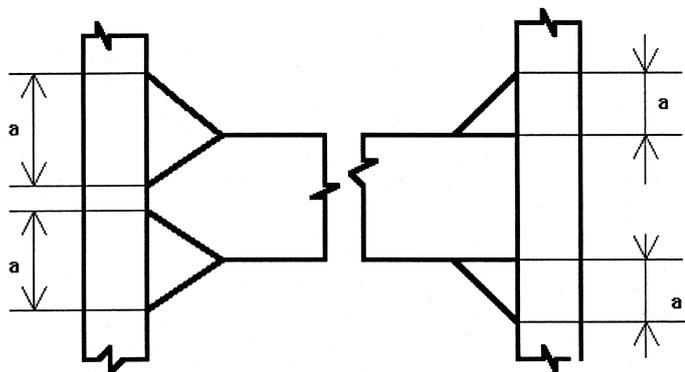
Definition von „a“ für die Schweißnahtarten 10 und 11
